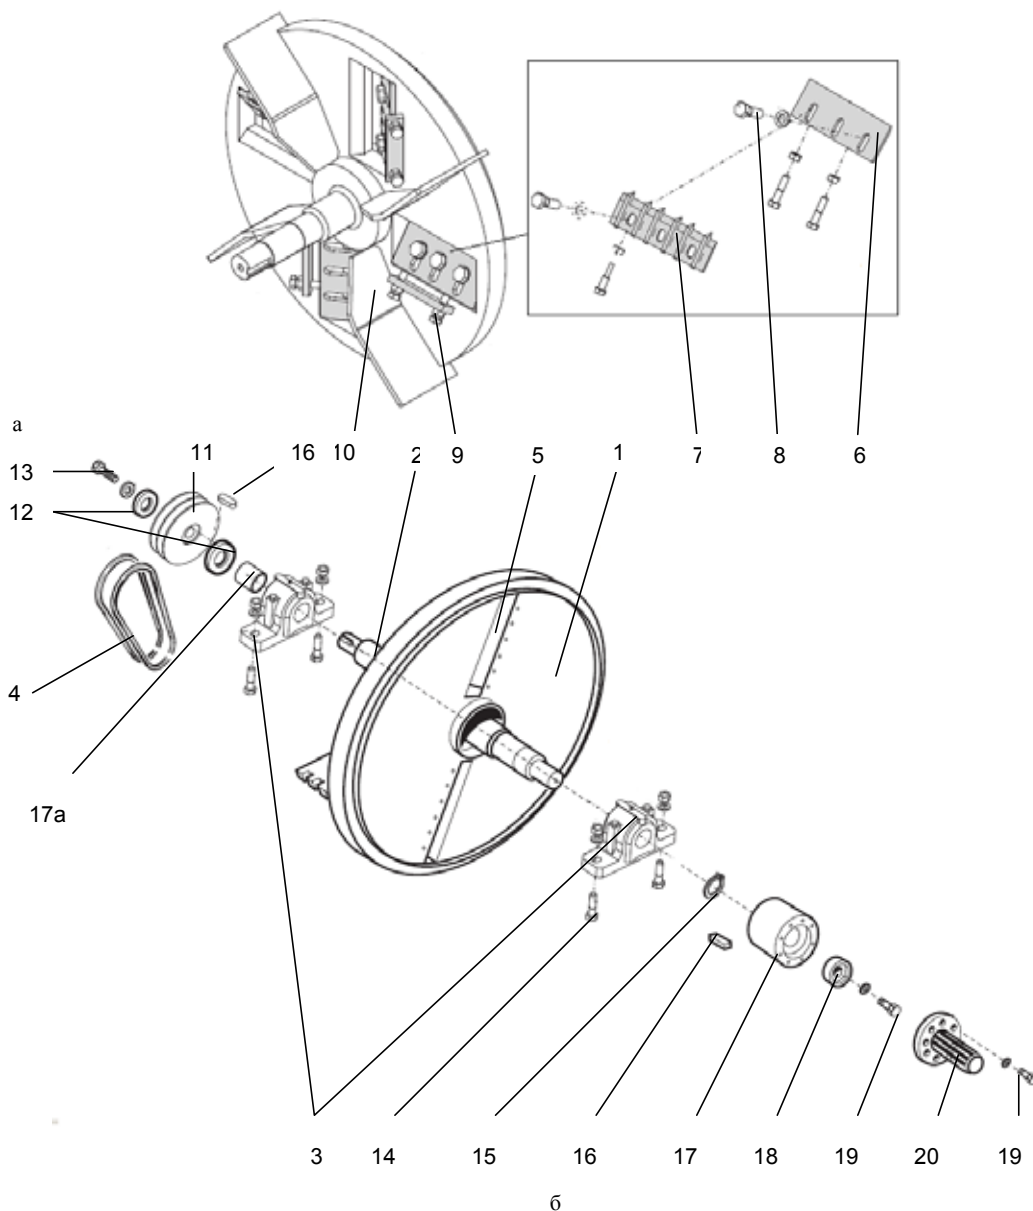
Ножевой диск в сборе на валу рубильной установки: а – Junkkari HJ260G/HJ 260 Gt; б – Junkkari HJ500C; 1 – ножевой диск; 2 – вал; 3 – корпус подшипников; 4 – клиновые ремни; 5 – окно для выхода щепы; 6 – нож; 7 – накладка; 8 – винт; 9 – винт регулировочный; 10 – лопатка вентиляционная; 11 – шкив; 12 – шайба; 13 – винт; 14 – винт; 15 – стопорное кольцо; 16 – шпонка призматическая; 17 – муфта; 17а – втулка; 18 – крепежный фланец; 19 – винт; 20 – шлицевой вал
